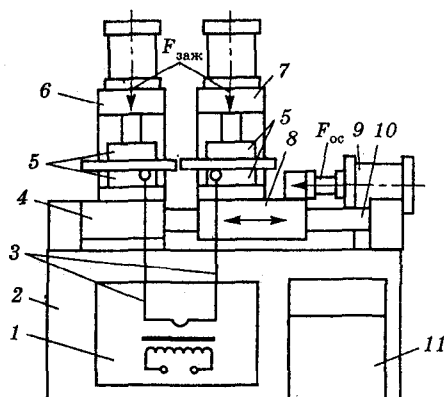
Конструктивная схема машины для стыковой сварки
